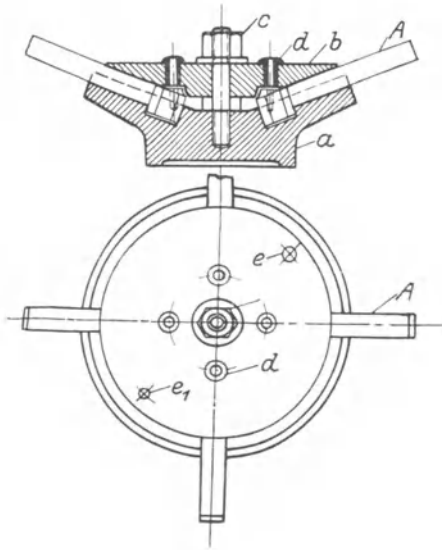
Bohrvorrichtung für Stahlhalter unter einem vierspindligen Bohrkopf.
